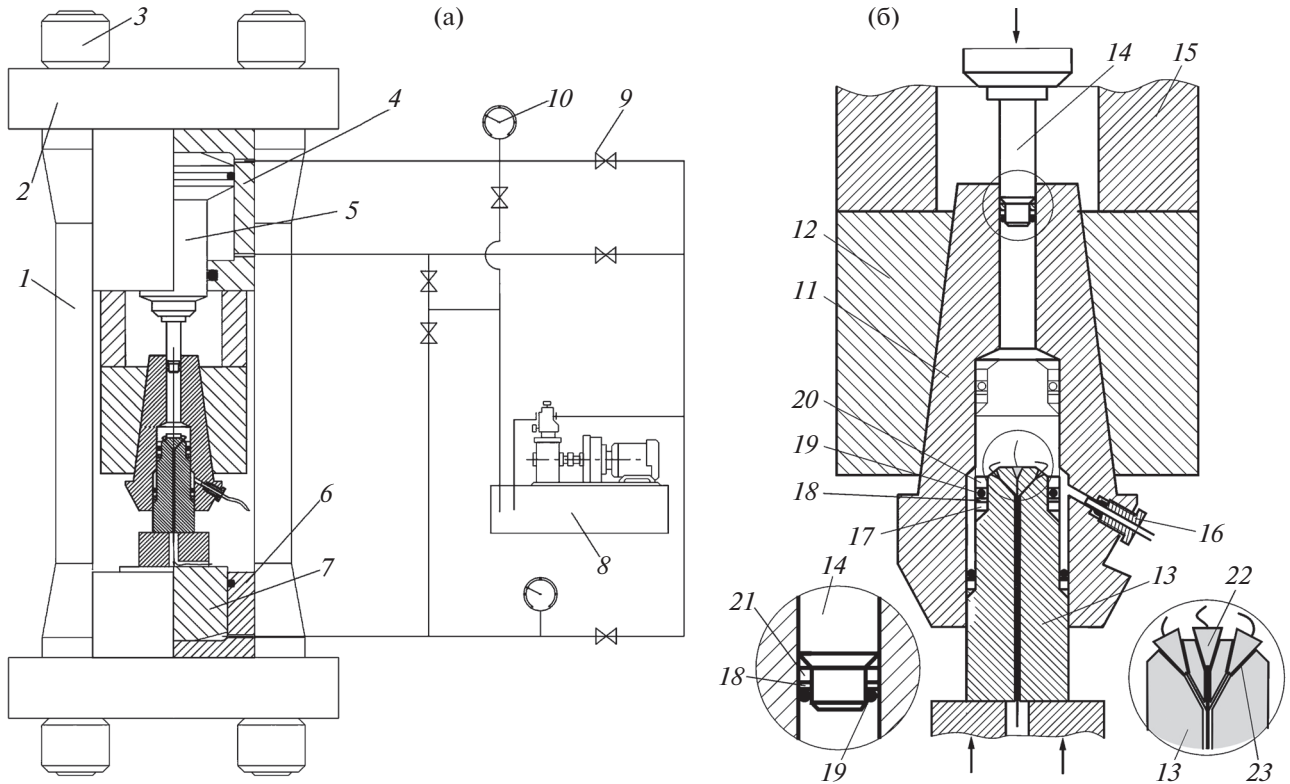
Общий вид установки (а) и камера высокого давления (б), находящаяся во внутреннем пространстве пресса. 1 – колонны; 2 – плиты; 3 – гайки; 4 – верхний цилиндр; 5 – верхний поршень; 6 – нижний цилиндр; 7 – нижний поршень; 8 – насос; 9 – вентили; 10 – манометры; 11 – камера; 12 – поддерживающая оправка; 13 – пробка; 14 – поршень; 15 – упорное кольцо; 16 – газовый ввод; 17 – стальное кольцо; 18 – индиевая прокладка; 19 – O-образное резиновое кольцо; 20 – стальное фиксирующее кольцо; 21 – кольцо из бериллиевой бронзы; 22 – стальные конусы; 23 – пирофиллитовая изоляция.
